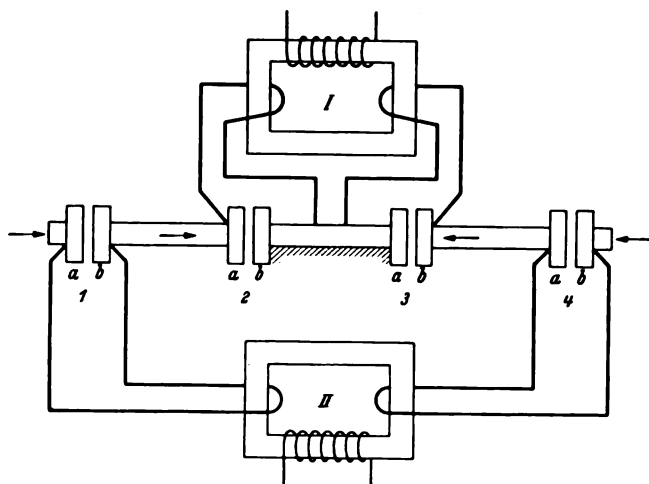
Zuordnung der beiden Umspanner zu den vier Schweißstellen.
